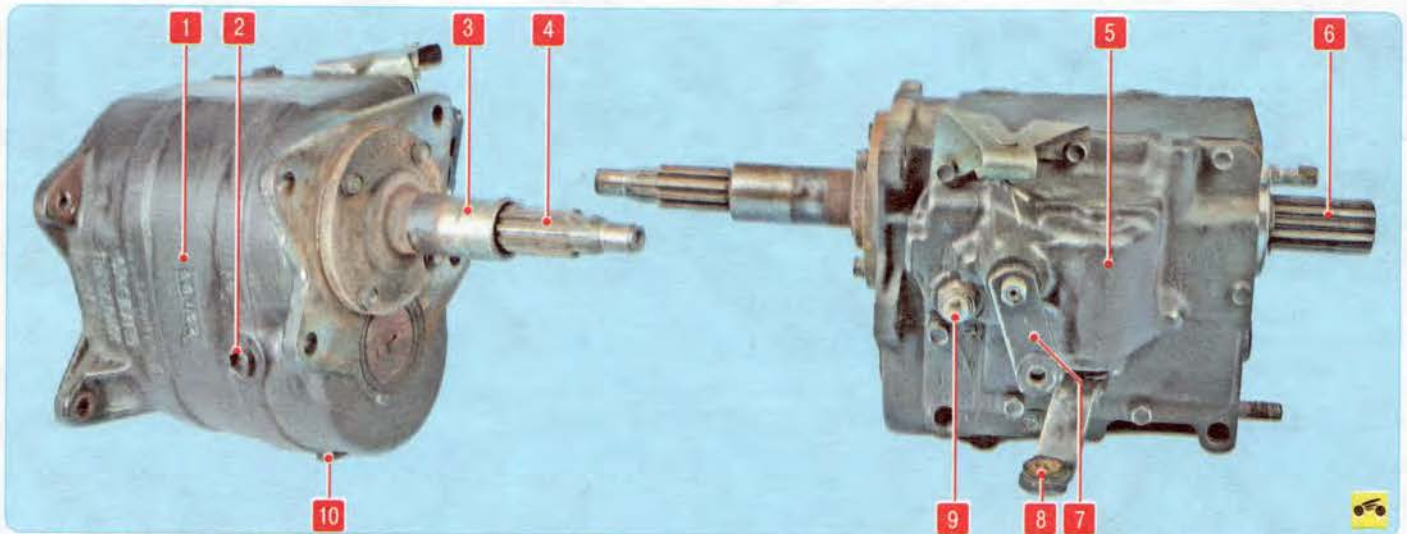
Коробка передач УАЗ 452-1700010-10: 1 – картер коробки передач; 2 – пробка наливного отверстия; 3 – передняя крышка первичного вала; 4 – первичный вал; 5 – механизм переключения передач; 6 – вторичный вал; 7 – рычаг выбора передач; 8 – рычаг включения передач; 9 – выключатель света заднего хода; 10 – пробка отверстия для слива масла
